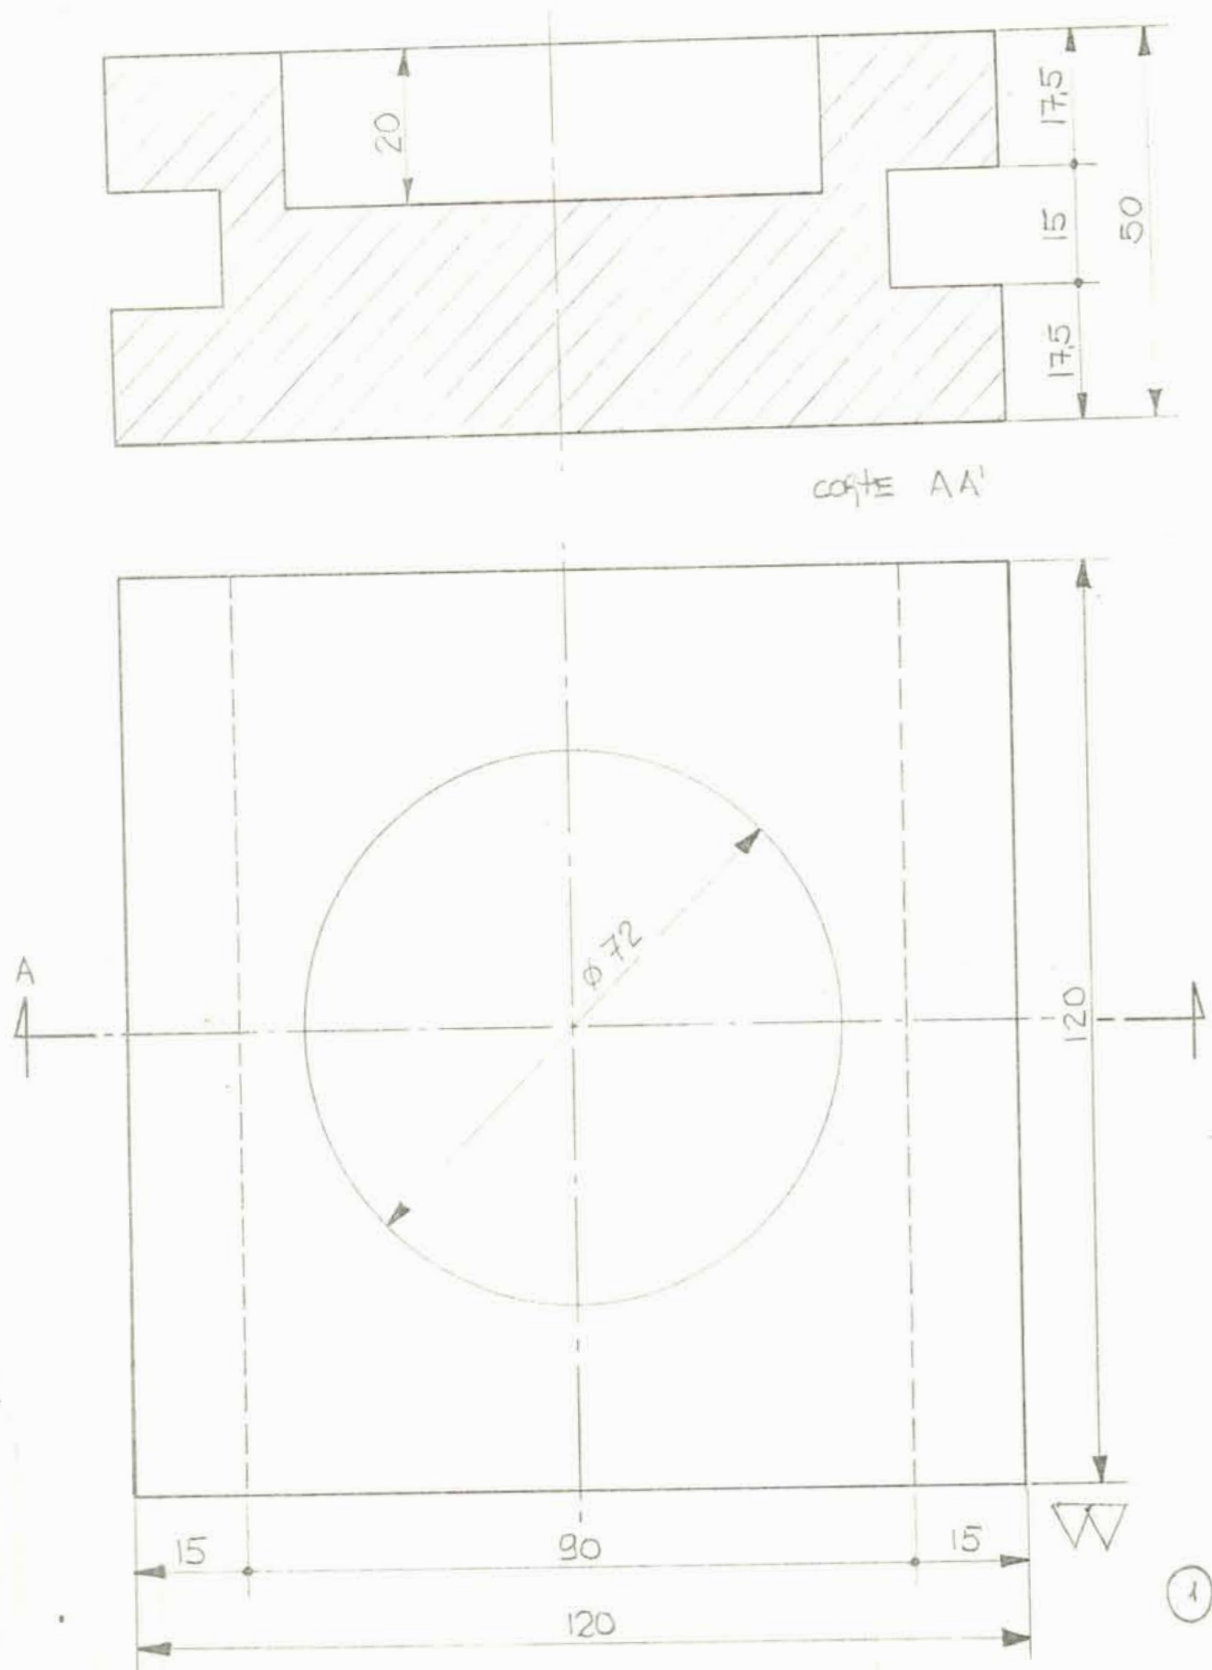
(b) - Vista em corte da base do dispositivo de compressão
